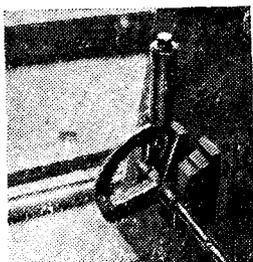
Манетка ограничителя оборотов двигателя МГ-17
